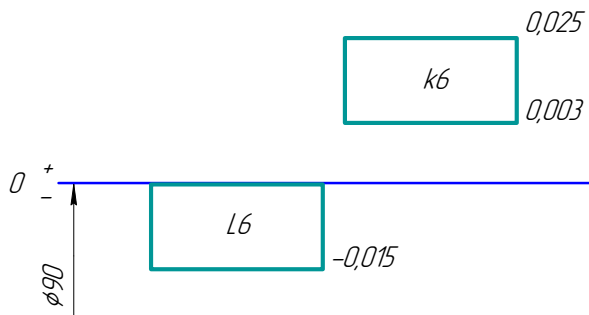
Схема расположения полей допуска посадки внутреннего кольца подшипника
